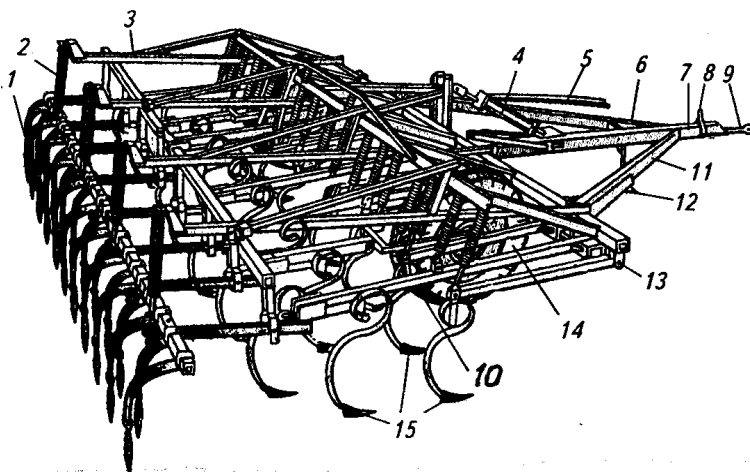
Культиватор КПС-4Г: 1 – звено зубовой бороны; 2 – штанга с пружиной; 3 – кронштейн навески; 4 – гидроцилиндр; 5 – штанга гидравлической системы; 6 – левая сница; 7 – центральная тяга; 8 – штангодержатель; 9 – прицепная серьга; 10 – грядиль; 11 – правая сница; 12 – подножка; 13 – рама; 14 – опорное колесо; 15 – стрелчатые лапы
